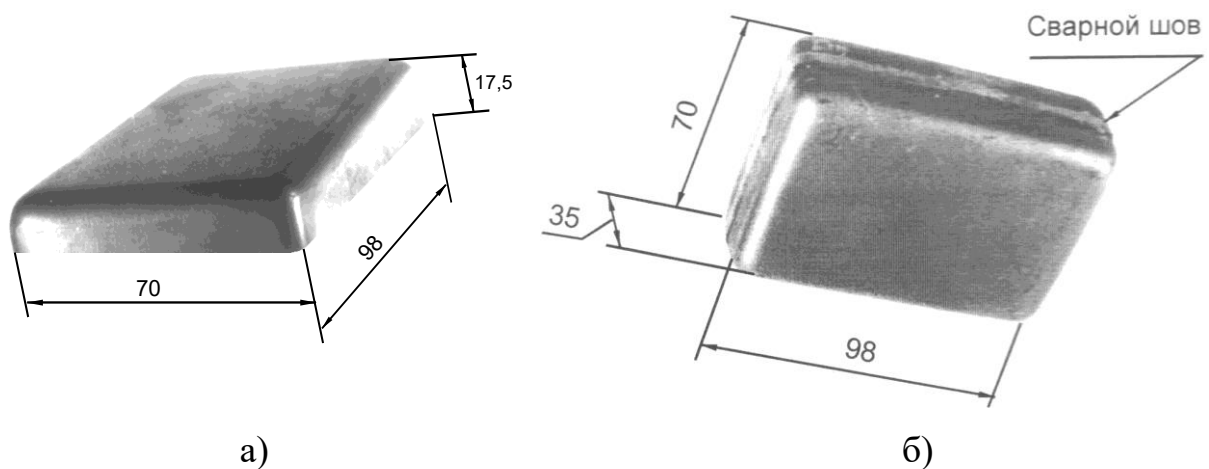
Вид штампованої заготовки-короба для виготовлення контейнера (а) і звареного контейнера для опромінення зразків-свідків (б)
